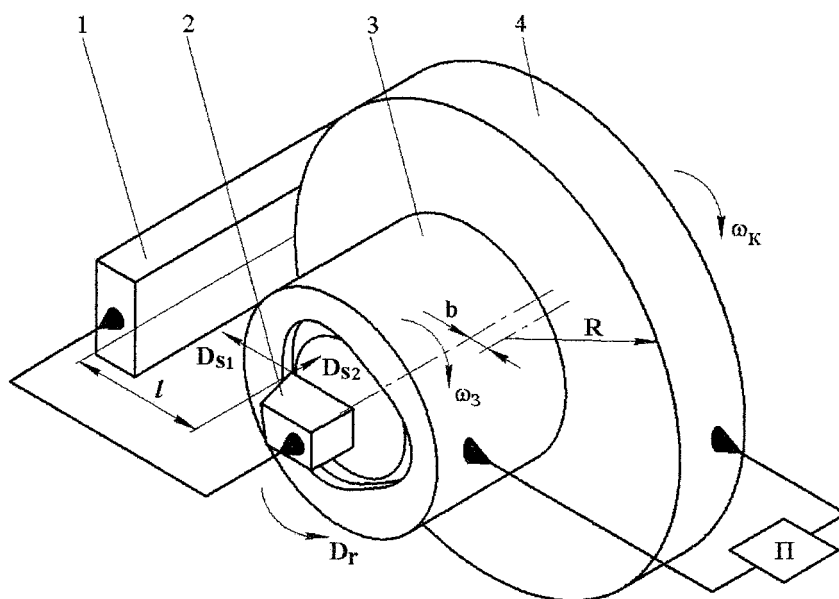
Схема обработки: 1 – шуп, 2 – резец, 3 – заготовка, 4 – копир
